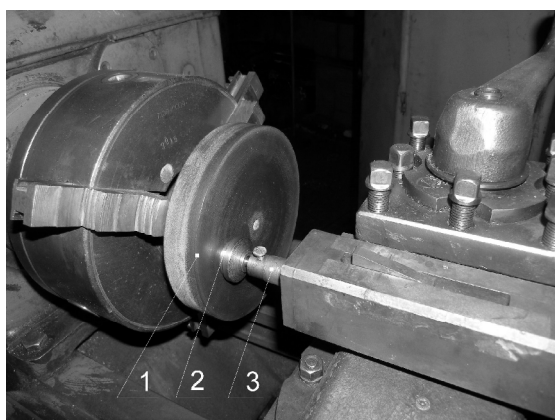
Алмазная доводка образцов титанового сплава на притире из текстолита: 1 – притир; 2 – образец; 3 – упругая державка
